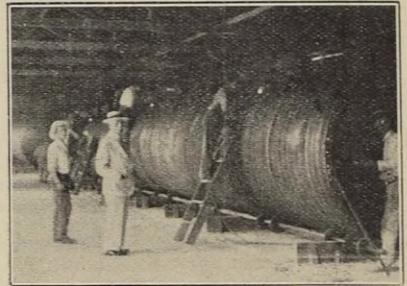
Fabrication par soudure autogène des éléments de tube de 22 mètres
